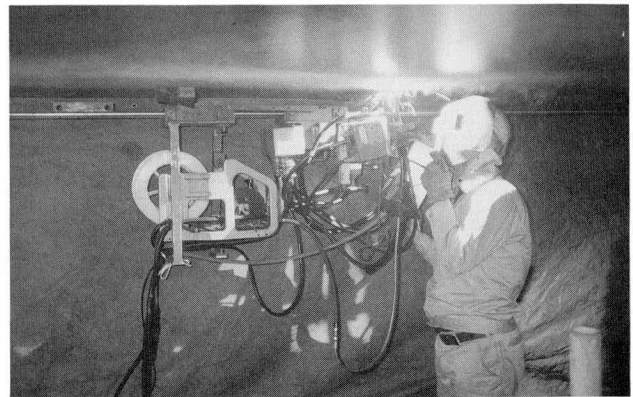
ガスシールド片面裏波自動溶接状況
